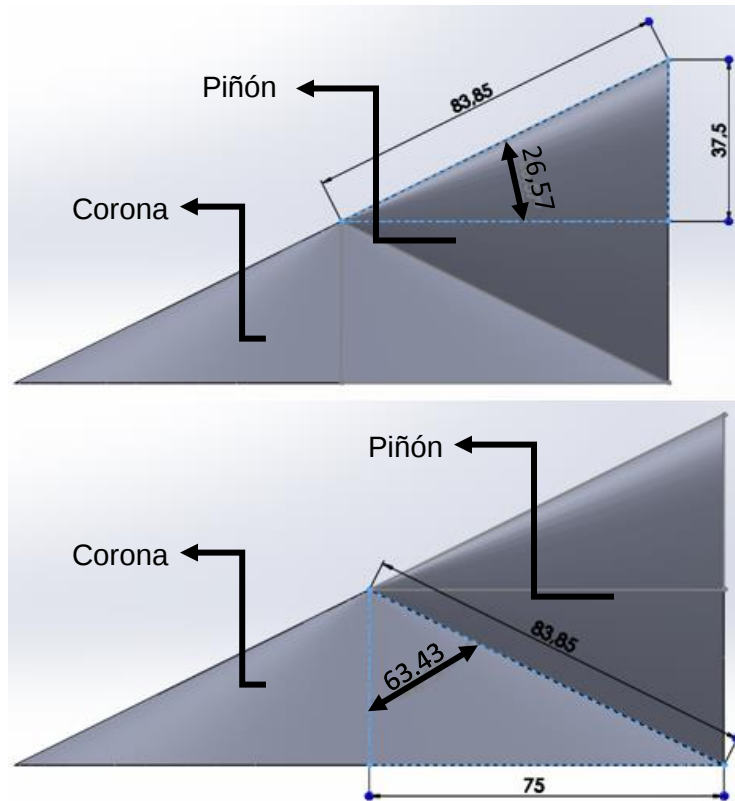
Dimensiones cono de paso par cinemático. Fuente Autor
